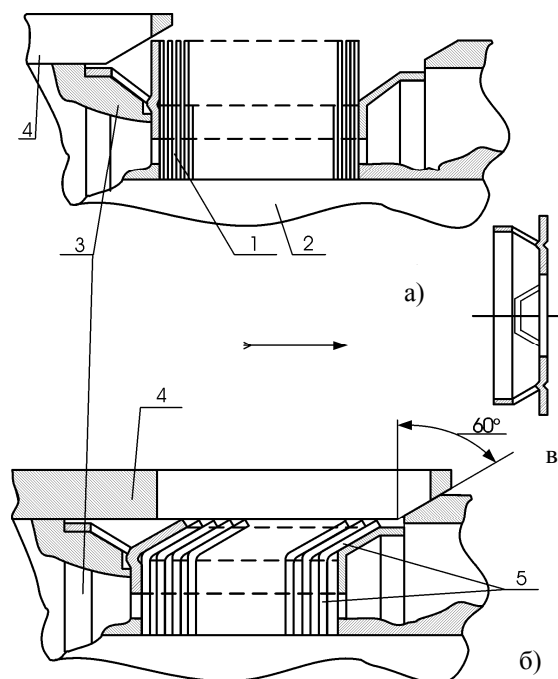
Приспособление формовки многоплоскостного магнитопровода: а – исходная позиция; б – конечная позиция; в – нажимной элемент
